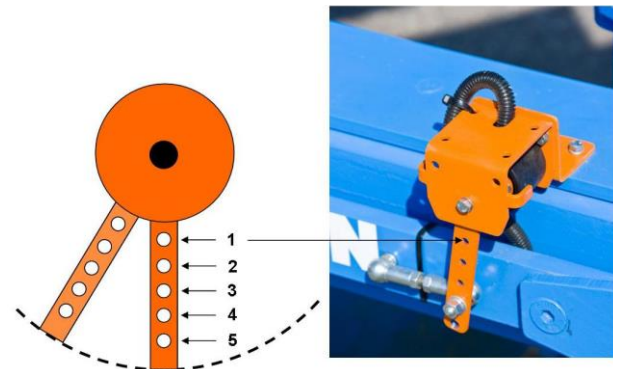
Hoeksensor bracket recht met twee stukken draadeind geklemd om hoofd-framebalk
